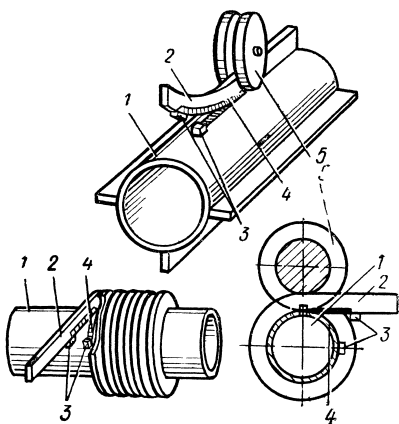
Приварка ребер к трубам с помощью контактной сварки ТВЧ: 1 — труба; 2 — ребро; 3 — токоподводящие контакты; 4 — путь тока; 5 — прижимный ролик
